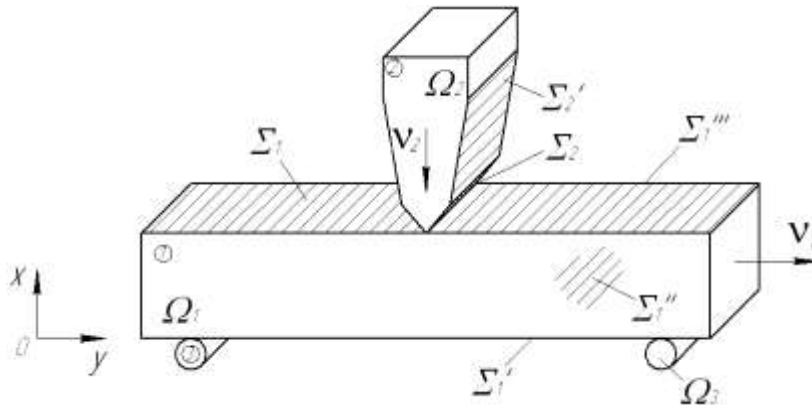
Схема різання безперервнолітої заготовки одним ножом:
